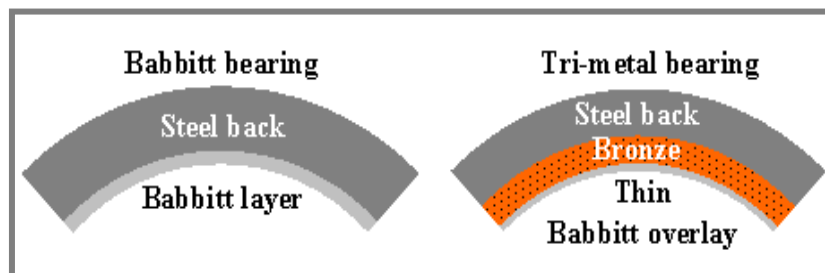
Materiály a řazení vrstev motorových kluzných ložisek [2].
